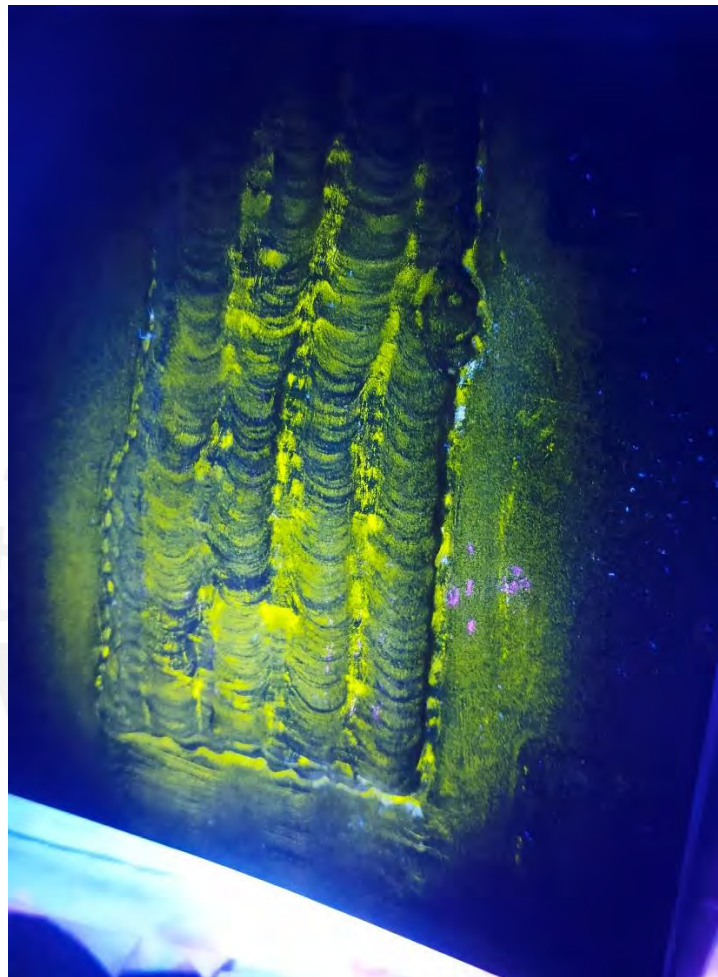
Superficie de soldadura ensayada con partículas magnéticas.
